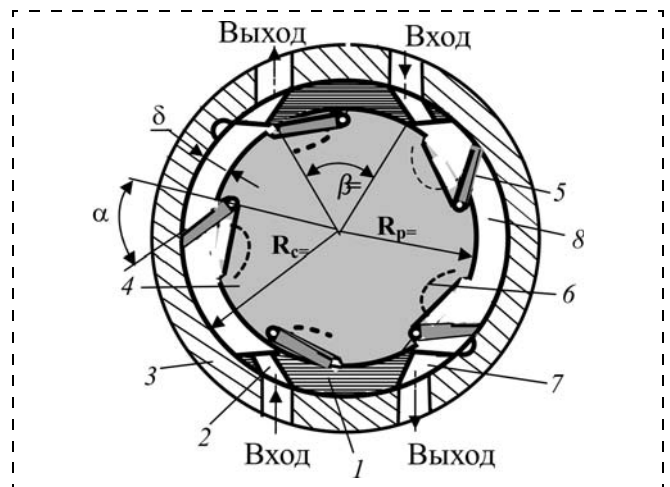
Сечение А-А по рис. 2 гидродвигателя ДМ:
